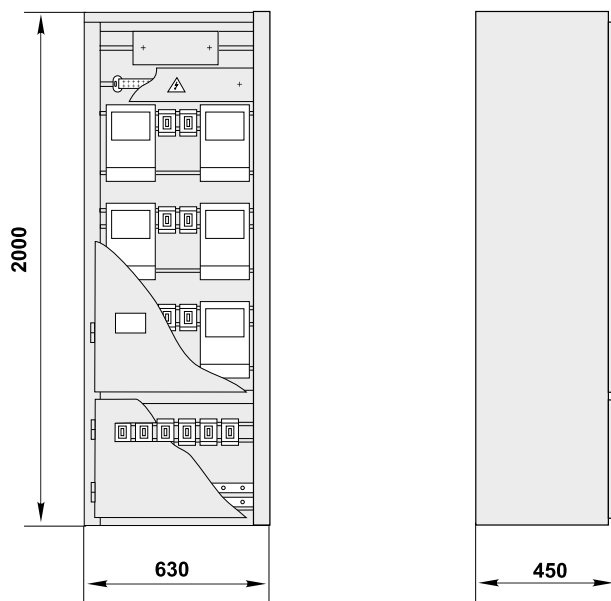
Габаритные размеры устройства ЗУР-200
